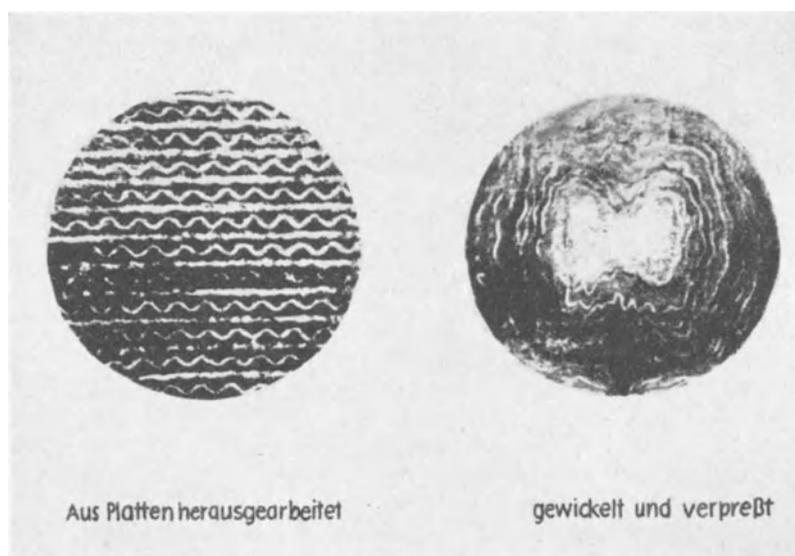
Querschnitt durch Stangen aus Hartgewebe
